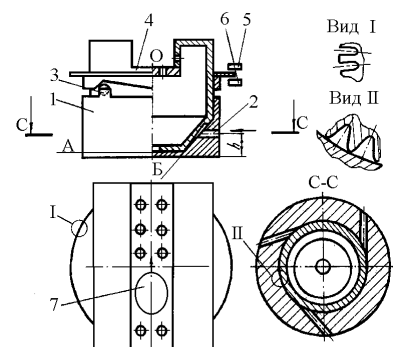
Устройство для бесконтактных взвешивания и сортировки штучных изделий по массе: 1 - корпус; 2 - дроссели для подачи сжатого воздуха; 3 - шаровая опора; 4 - промежуточная платформа-ротор; 5 - световой излучатель; 6 - фотозлемент; 7 - изделие.
